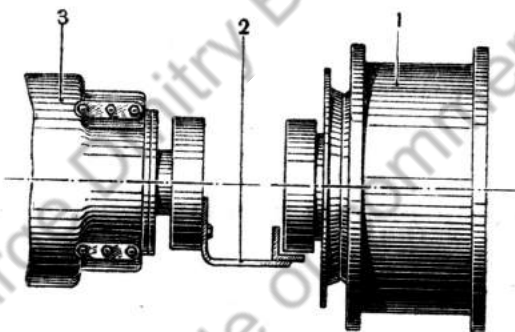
Центровка коробки перемены передач при установке её в танк:
